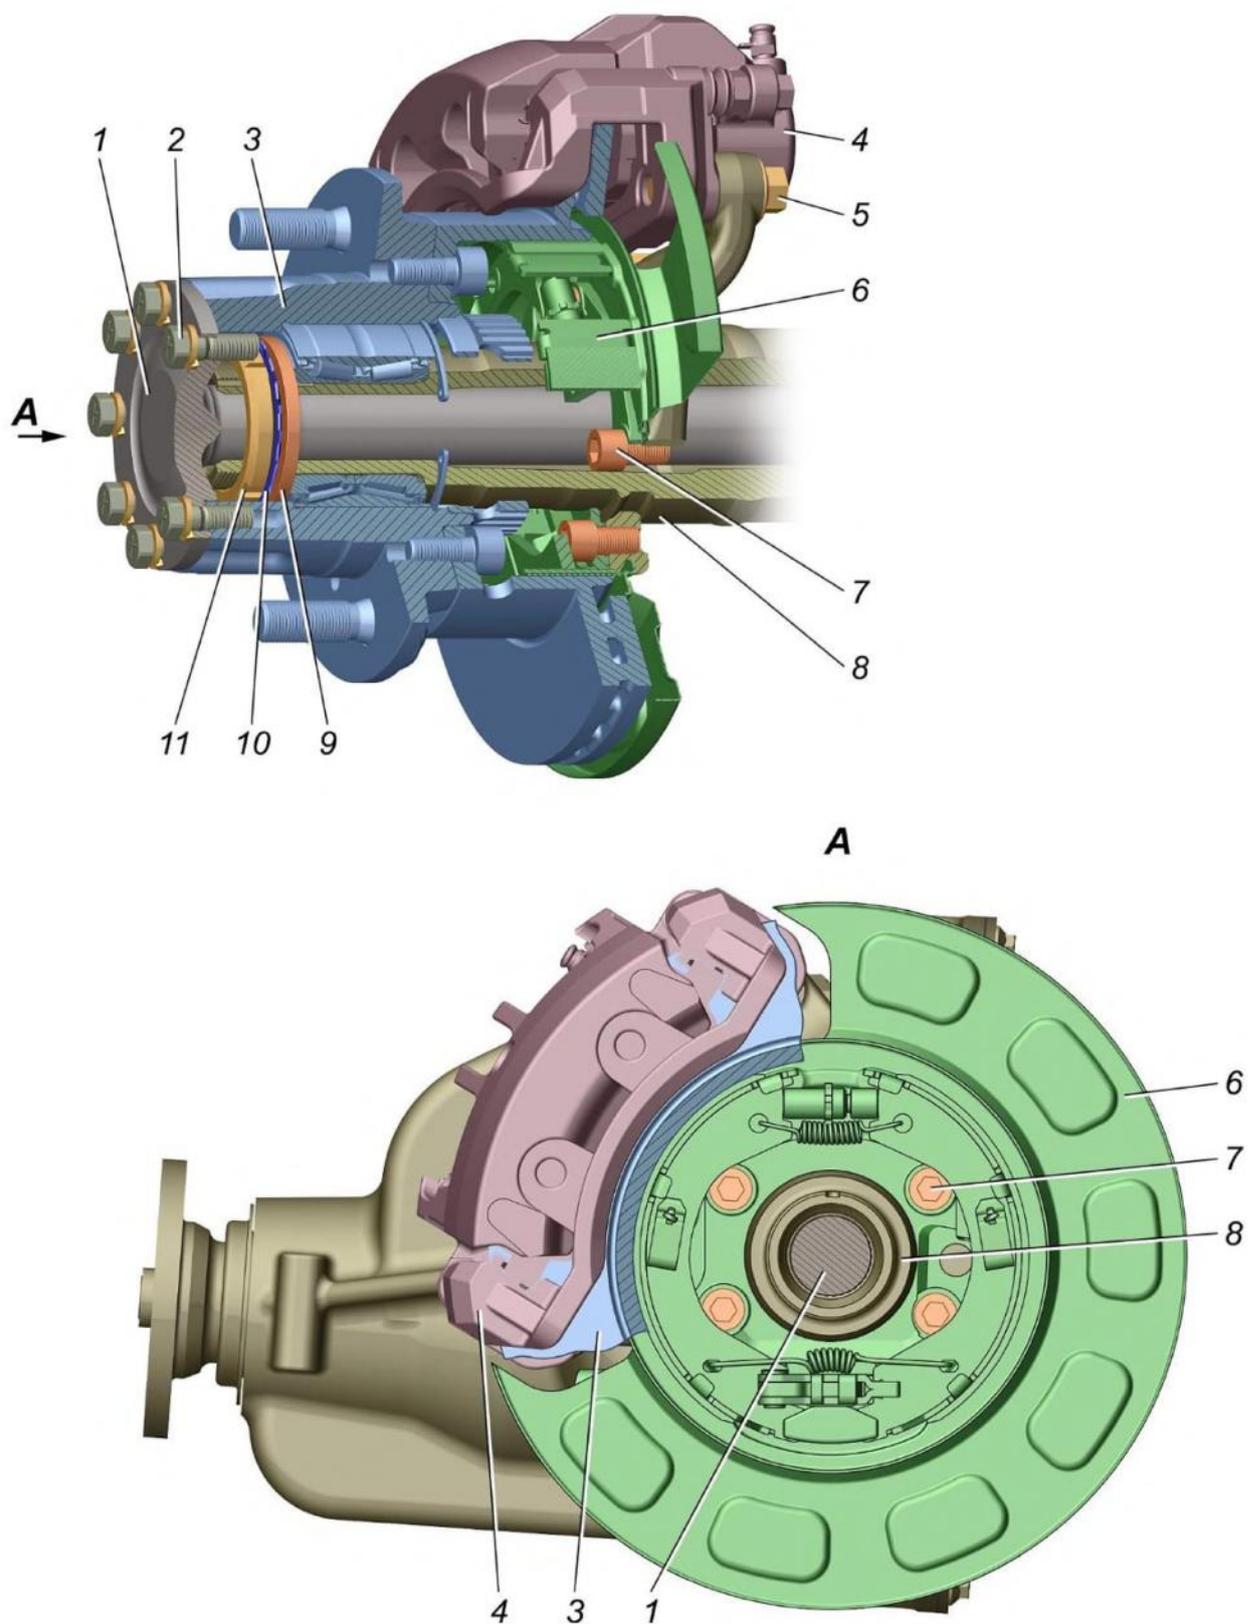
Задний мост (ступица часть): 1 – полуось заднего моста; 2,5 - болты; 3 - ступица заднего колеса с тормозным диском и подшипником; 4- тормоз дисковый левый; 6 – тормоз стояночный левый; 7 – винты; 8- кожух полуоси 9 – шайба упорная; 10 - шайба стопорная; 11- гайка шлицевая
